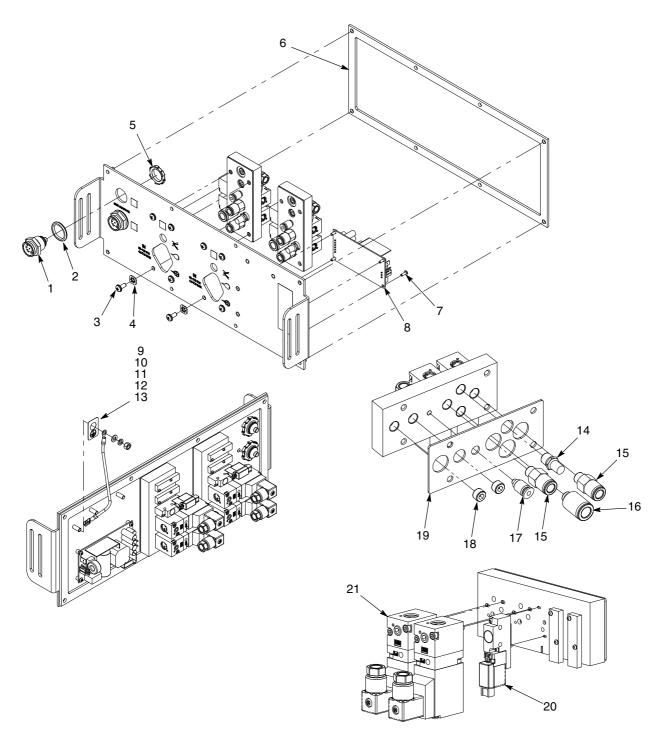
Pezzi del sottogruppo del pannello posteriore - Controller di due e più pistole
